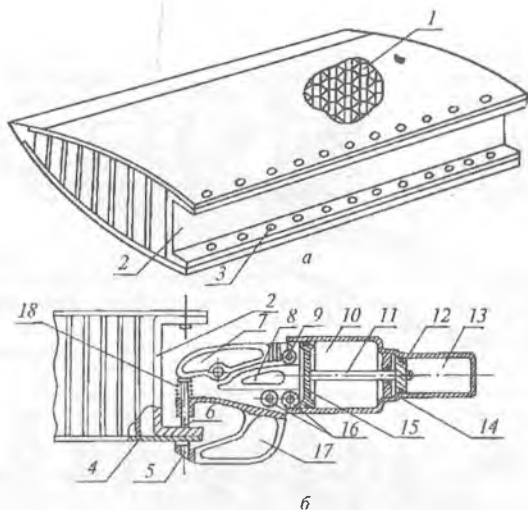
Схема клепки пневморычажным переносным прессом: а — изделие с клееным сотовым наполнителем, которое клепают переносным прессом; б — схема клепки прессом: 1 — сотовый наполнитель; 2 — лонжерон; 3 — заклепка; 4 — обшивка; 5 — обжимка; 6 — пуансон; 7 — рычаг; 8 — клин; 9, 16 — подшипники; 10, 13, 14 — рабочие полости цилиндров; 11 — шток; 12, 15 — поршни; 17 — скоба; 18 — пружина
